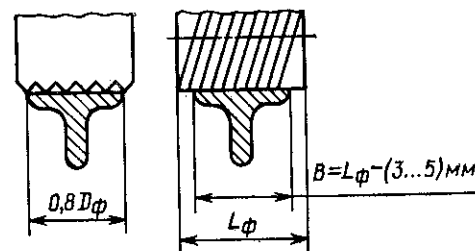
Учет стандартного размера фрез при оформлении чертежа
